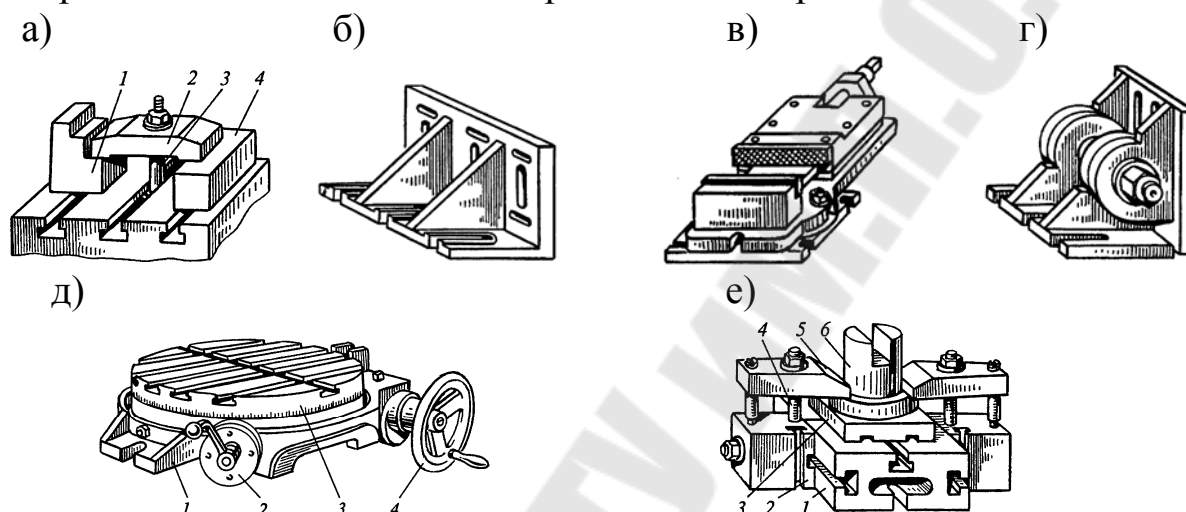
Устройства и приспособления для установки и закрепления заготовок:
